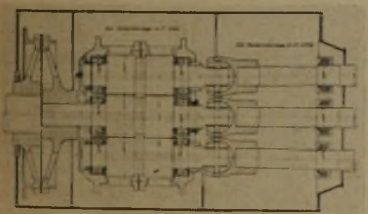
Längsschnitt des Kammwalzgerüsts einer 500er-Straße
